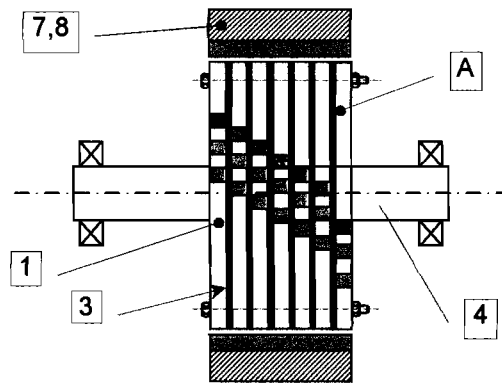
Motor magnetic cu pornire/oprire radială, cu număr de magneți de pe rotor diferit de numărul de magneți de pe stator (nr. de rotoare dintr-un grup este de minimum 7 buc).
